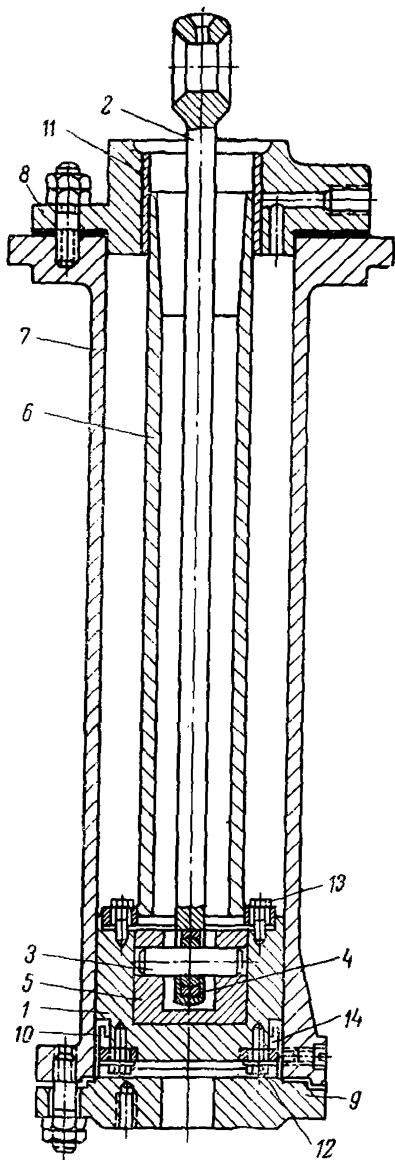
Приводной цилиндр конструкции 1954 г.:
